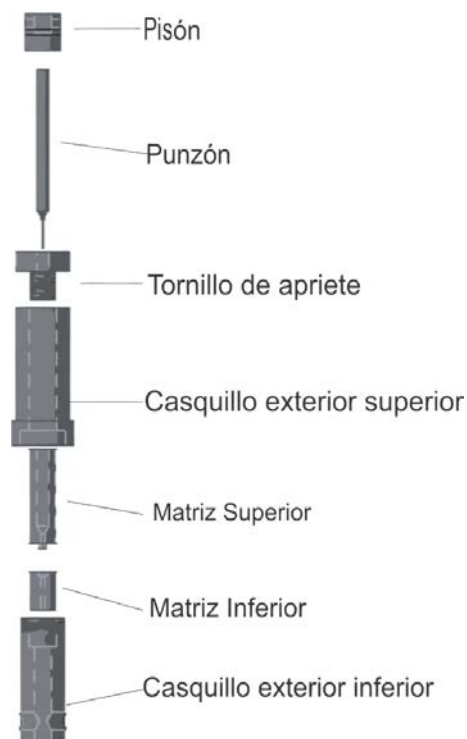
Utillajes se montan directo a la máquina, se agrega tornillo de apriete.
